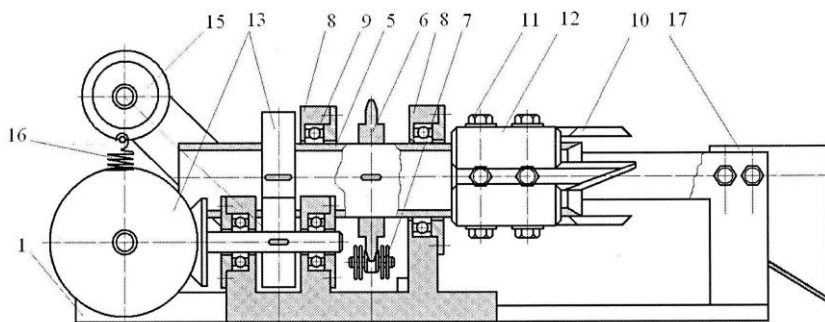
Устройство для заготовки хвойной лапки (вид сбоку)
